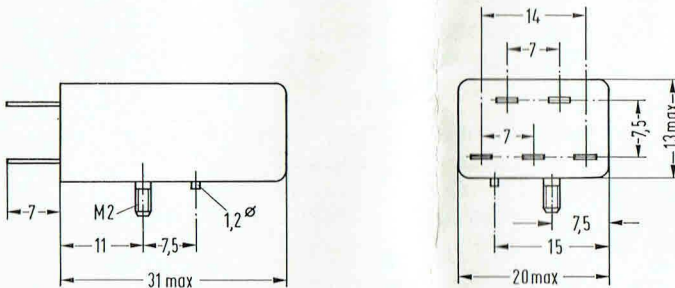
Relais V23016-A... pour cosse AMP 2,9x5mm ou connexions soudées.
